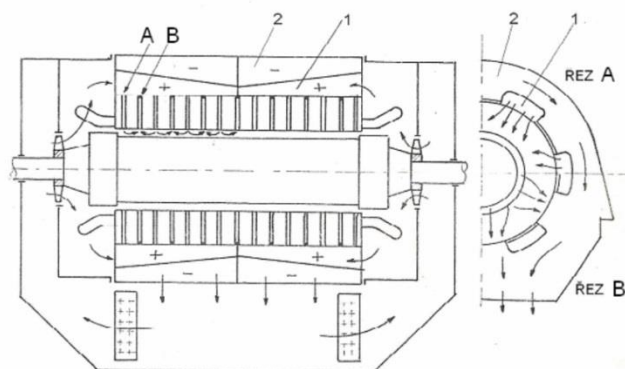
Komorový systém chlazení statorů (převzato z [6]);
